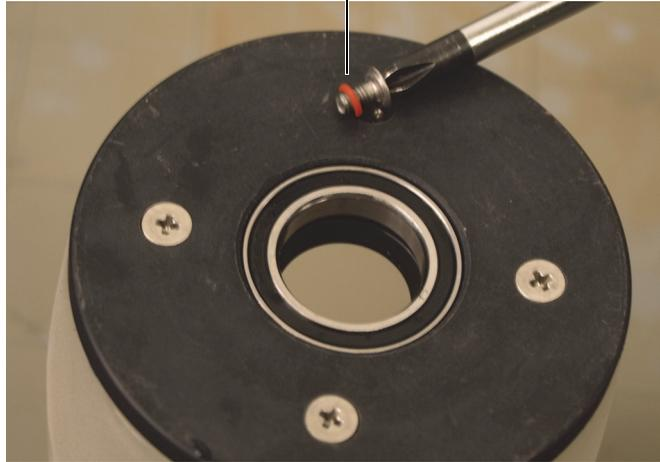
Entfernen der äußeren Halteschrauben vom Flachflansch der Akustikrolle
